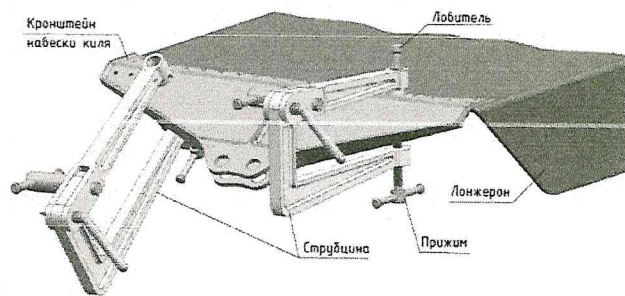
Общий вид кондукторной скобы-клещей, установленной на конструкции
